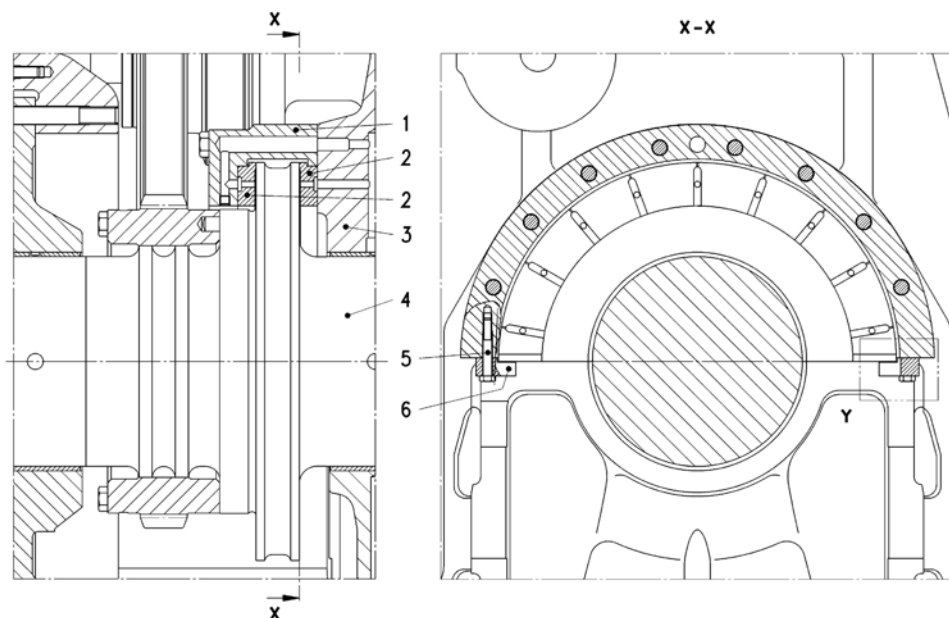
Колінчатий вал з упорним підшипником: 1 – корпус осевого підшипника; 2 – торцеві вкладиші; 3 – торцева кришка; 4 – колінчастий вал; 5 – бовти кріплення; 6 – упори
